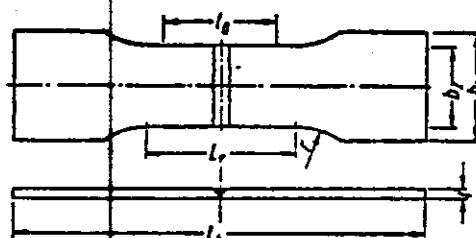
Zugprobe aus Schweißprobe 1
